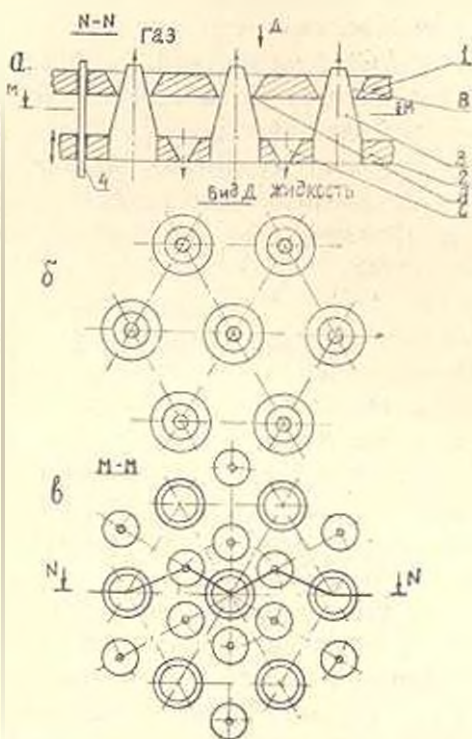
Пропальная тарелка с регулируемой площадью провала. 1 — верхняя пластина; 2 — нижняя пластина; 3 — коническая насадка; 4 — направляющий стержень; А — кольцевой зазор; В — отверстие верхней пластины; С — отверстие нижней пластины.
